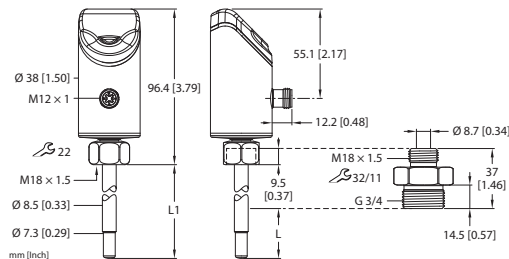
Abmessungen – Sensor mit Einschraubadapter G3/4"
